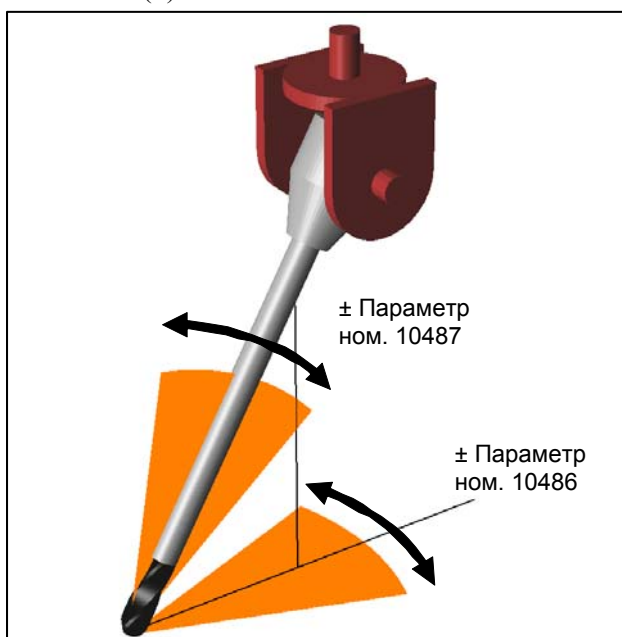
(d) Зона коррекции для станка с вращающейся инструментальной головкой
